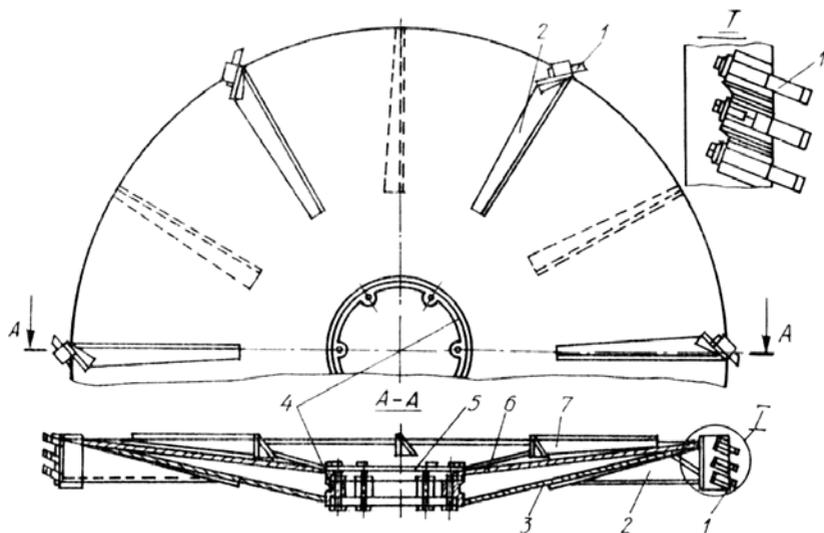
Фреза двухфрезерного экскаватора-каналокопателя:
